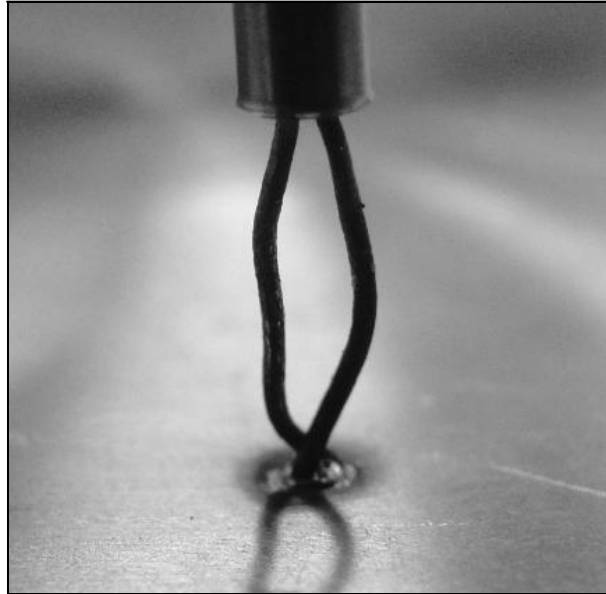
Condutores do termopar soldados ao material da base da solda por fricção.
